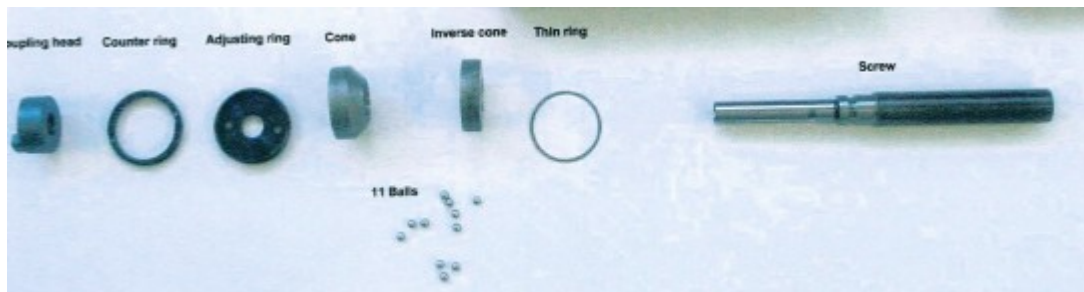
Detalle de las piezas interiores que componen cada tornillo-motor.
